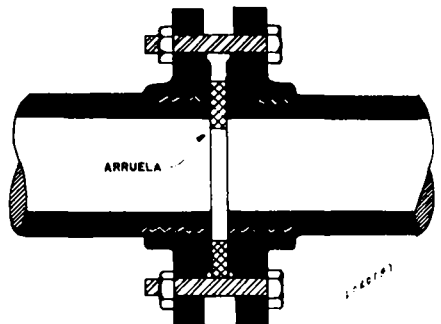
ARRUELA COM DIÂMETRO EXTERNO PEQUENO
